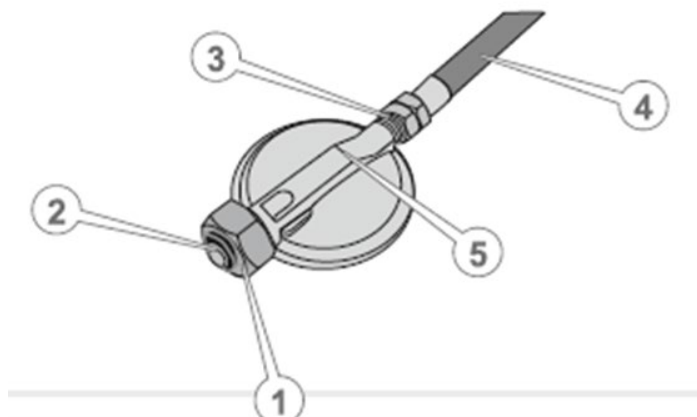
Загальний вигляд газового редуктора (редуктора тиску), під'єданого до газового рукава.
